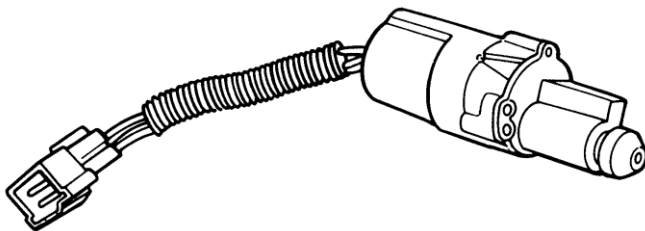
Устройство привода дроссельной заслонки: 1 - электрический разъем; 2 – контактный выключатель; 3 – защитный чехол; 4 – вал; 5 – шток; 6 - редуктор; 7 – электродвигатель постоянного тока
